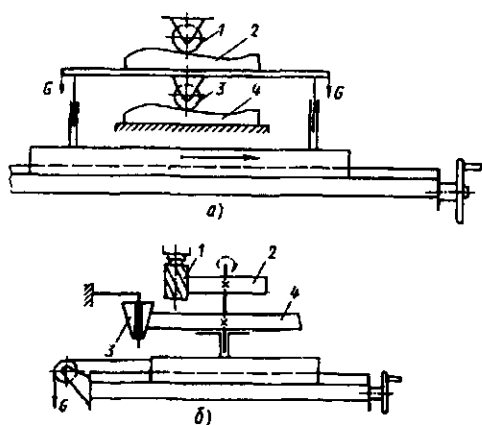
Схемы копирного фрезерования: а – с продольной задающей подачей; б – с круговой задающей подачей; 1 – фреза; 2 – заготовка; 3 – копирующий ролик; 4 – копир; 5 – груз
